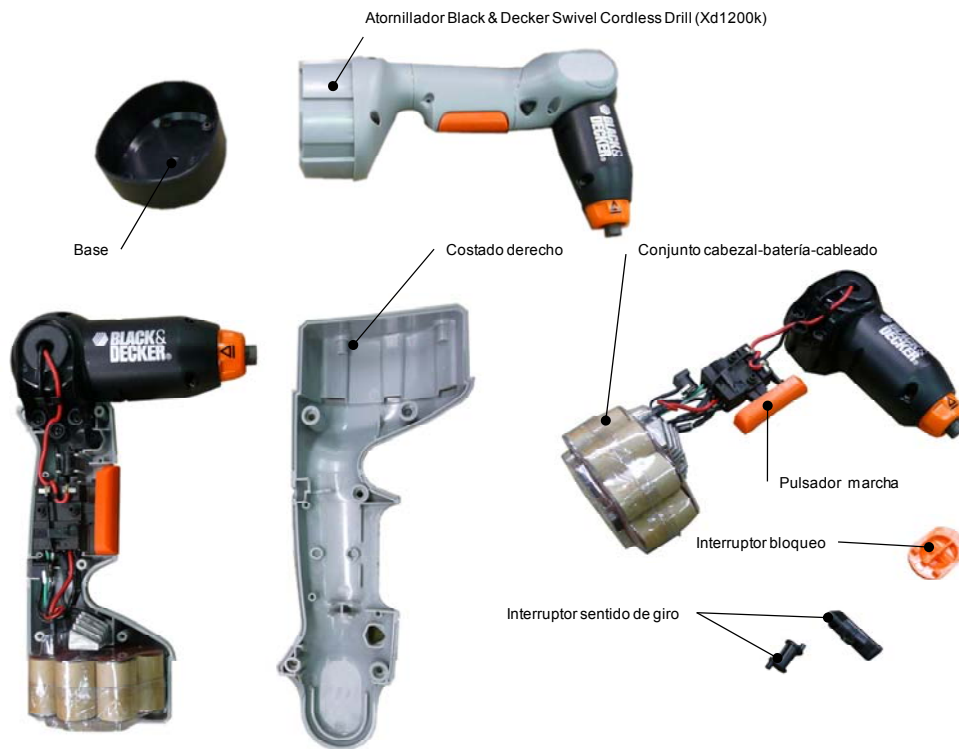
Destornillador Black & Decker Swivel Cordless Drill (Xd1200k)
